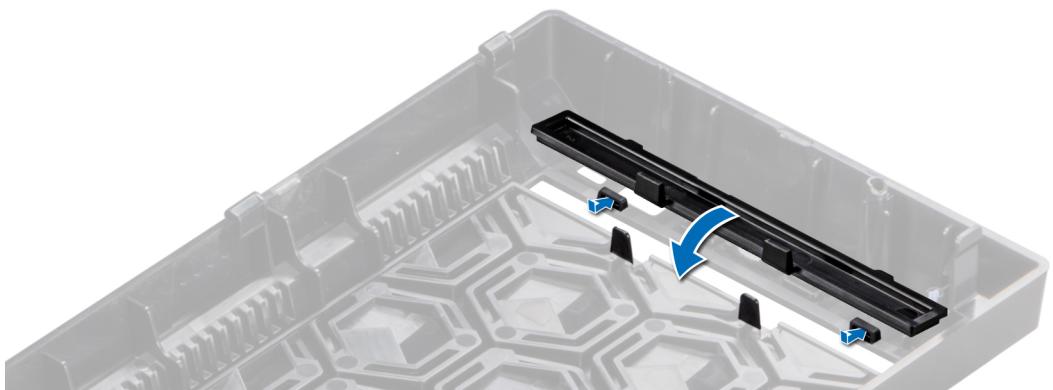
Installation de la plaque de recouvrement du lecteur optique sur le cadre avant
